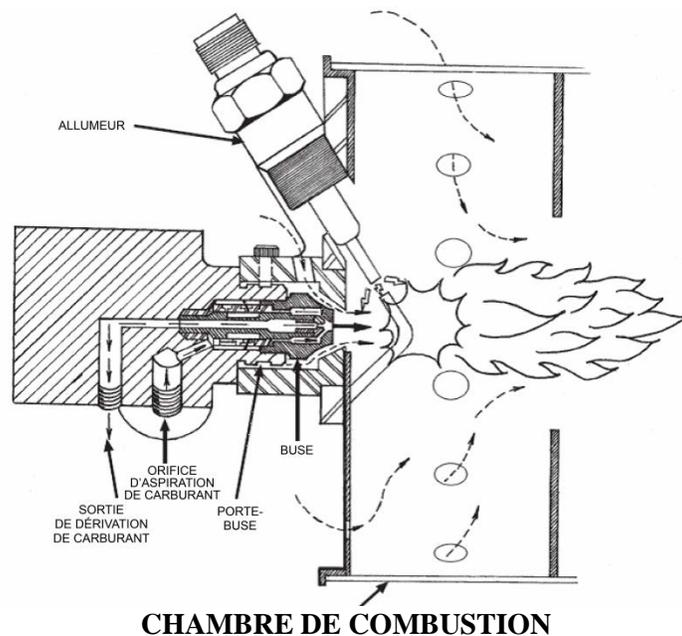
Vue en coupe de la buse et de la chambre de combustion
